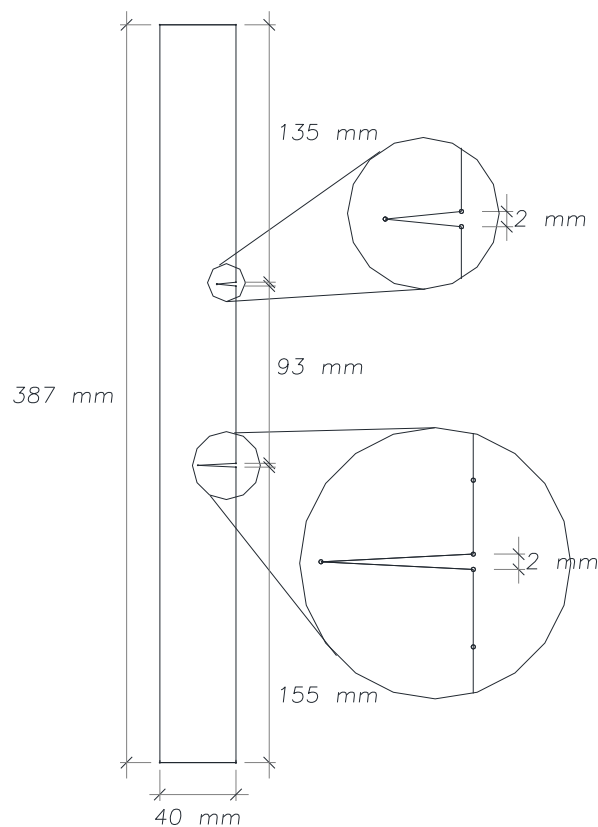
Geometria da placa retangular com duas fissuras angulares
